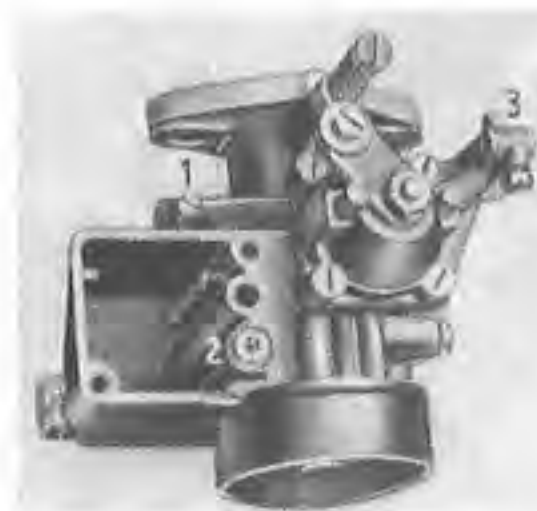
Karburátor 28HB3-1 (pohled zprava zpředu)
